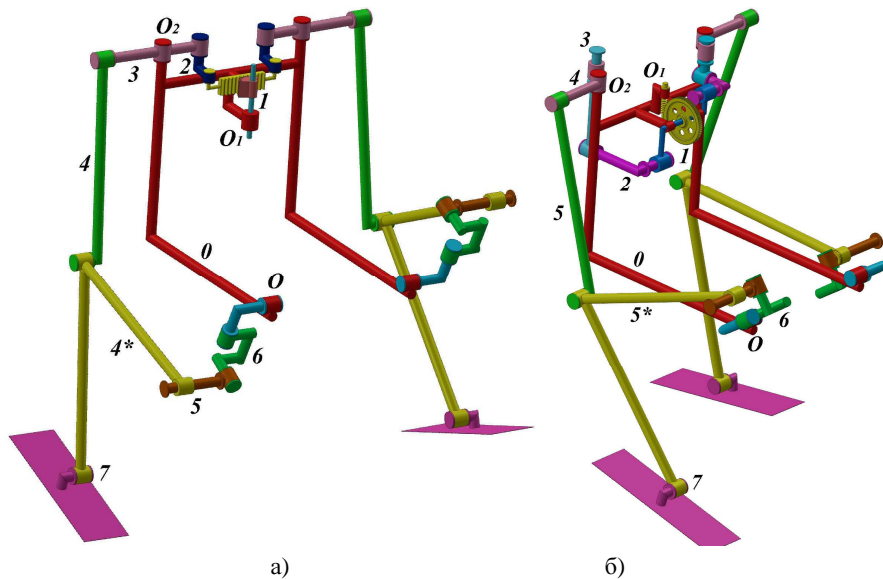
Принципова схема механізму повороту крокуючого модуля з двома цикловими рушійми: а) рейково-важільного; б) черв'ячно-важільного
